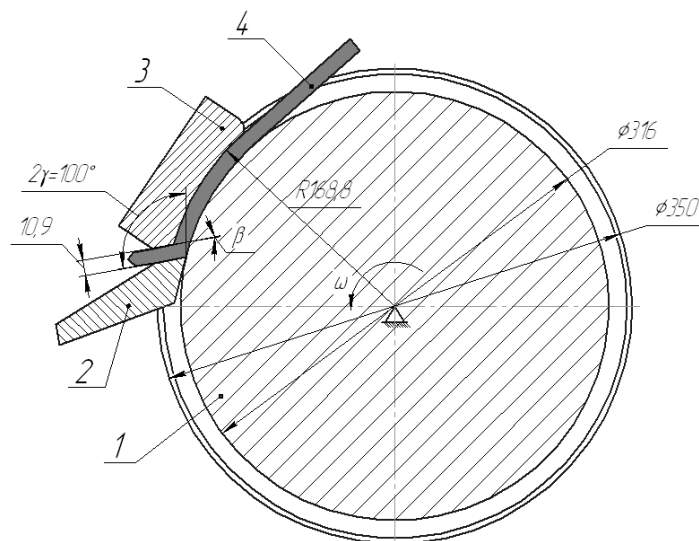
Схема инструмента РКУП-К для прессования заготовок прямоугольного сечения (1 – ротор; 2 – упор; 3 – прижим; 4 – заготовка).
